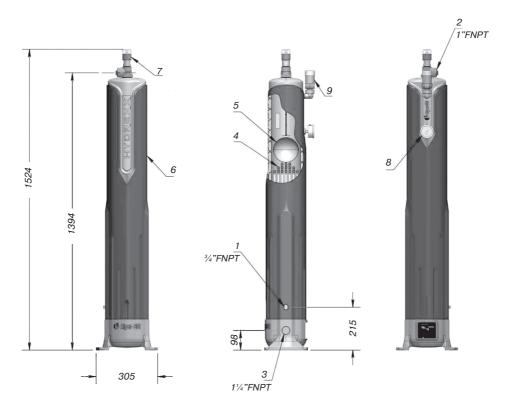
Испаритель Hydrexx: 1— вход жидкой фазы; 2— выход паровой фазы; 3— вход/выход теплоносителя; 4— теплообменник; 5— сферический поплавок; 6— изоляционный кожух; 7— выпускной клапан с ручным сбросом; 8— манометр; 9— предохранительный сбросной клапан
